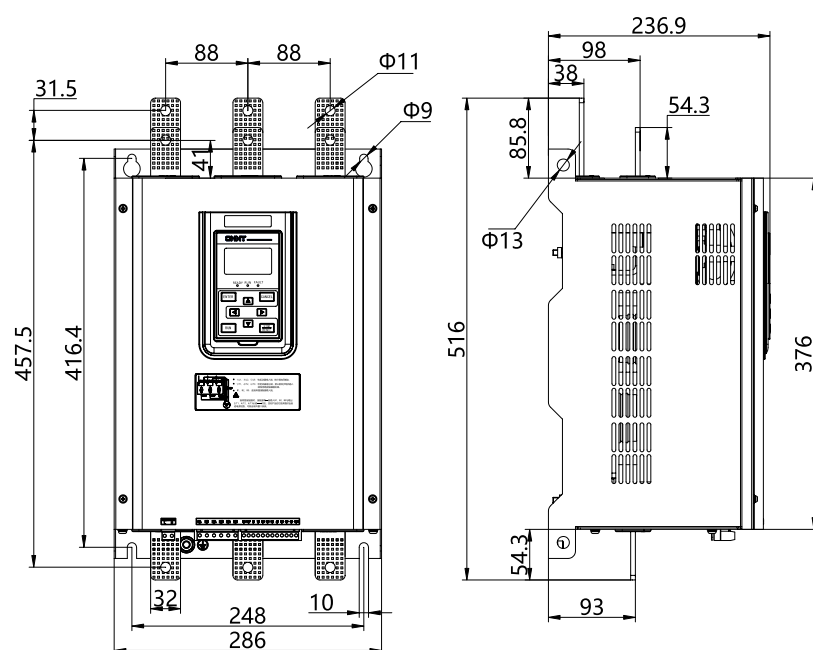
Общий компоновочный и установочный габаритный чертеж моделей NJRP5-180/D4-NJRP5-370/D4, NJRP5-180/D6-NJRP5-370/D6
